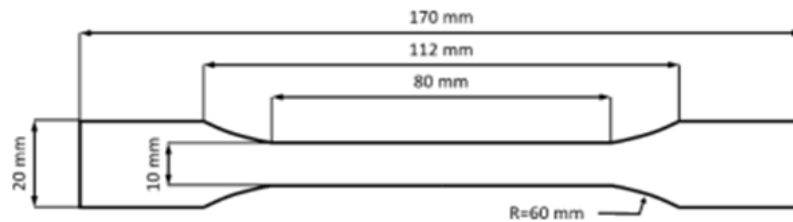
Dimensions des éprouvettes pour les essais quasi-statiques de la matrice PA11
